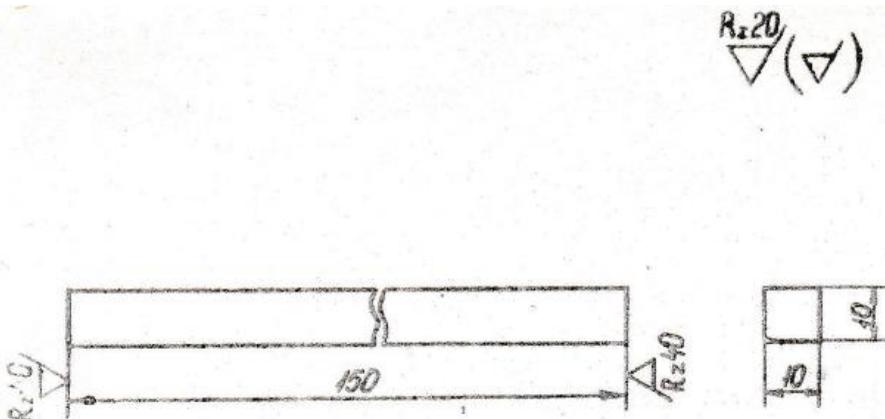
Форма и размеры стандартного образца из стали с твердостью 140...210 НВ
